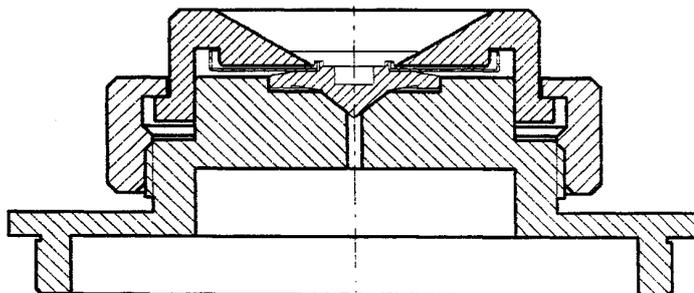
Оправка для установки свариваемой подборки под сварку электронным лучом
